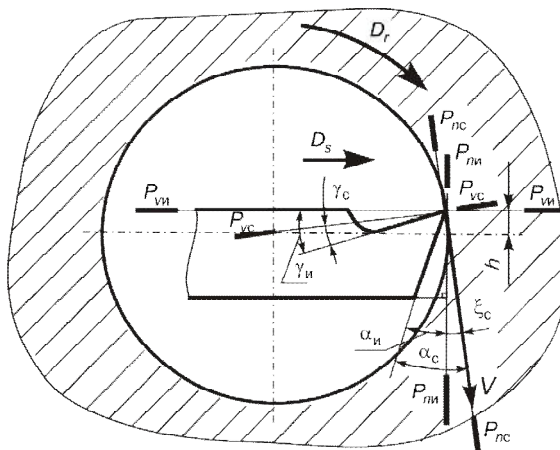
Особенности определения статических и инструментальных углов режущей части расточного резца при его установке выше оси заготовки
